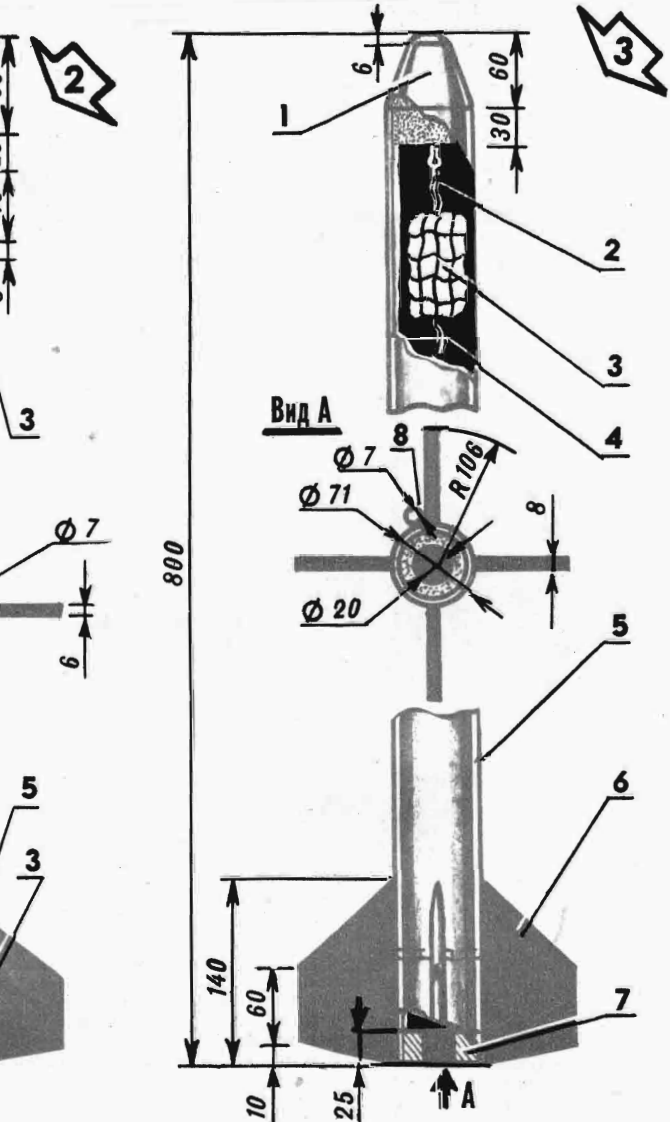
Модель ракеты «Родник»: 1 — головной обтекатель, 2 — нить, 3 — полезный груз, 4 — стропы парашюта, 5 — корпус, 6 — стабилизатор, 7 — обoйма, 8 — направляющее кольцо.
